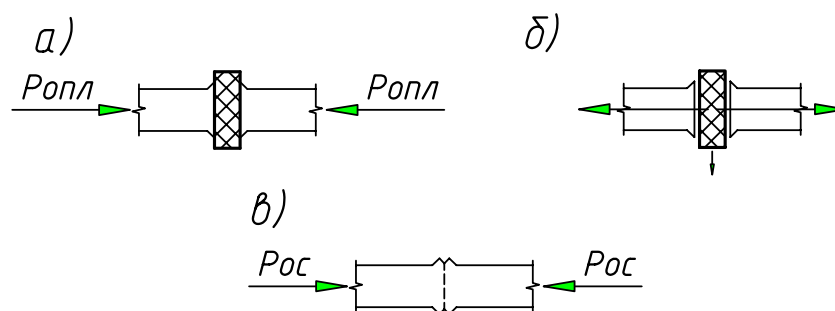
Циклы контактной сварки с помощью нагретого элемента: а) нагрев (оплавление) свариваемых поверхностей; б) удаление нагревательного элемента (технологическая пауза); в) соединение (осадка) свариваемых поверхностей
